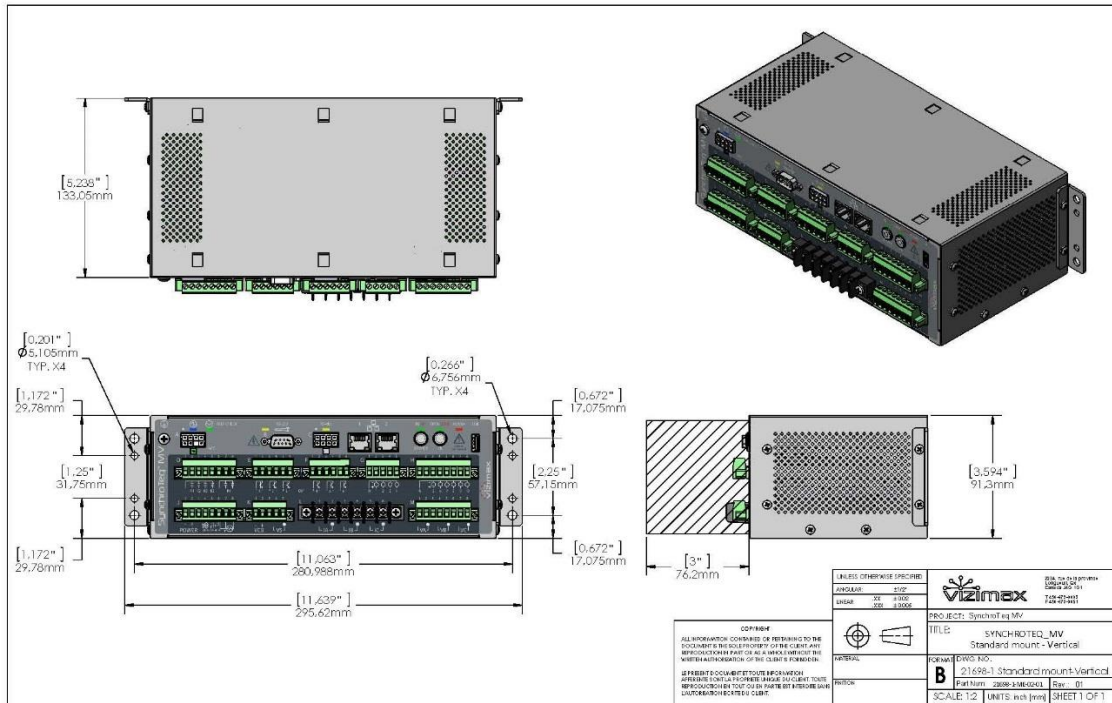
INSTALLATION STANDARD – VERTICALE
